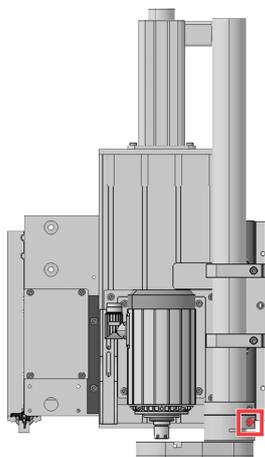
FESTZIEHEN DER SCHRAUBE DES SAUGSCHUHS
